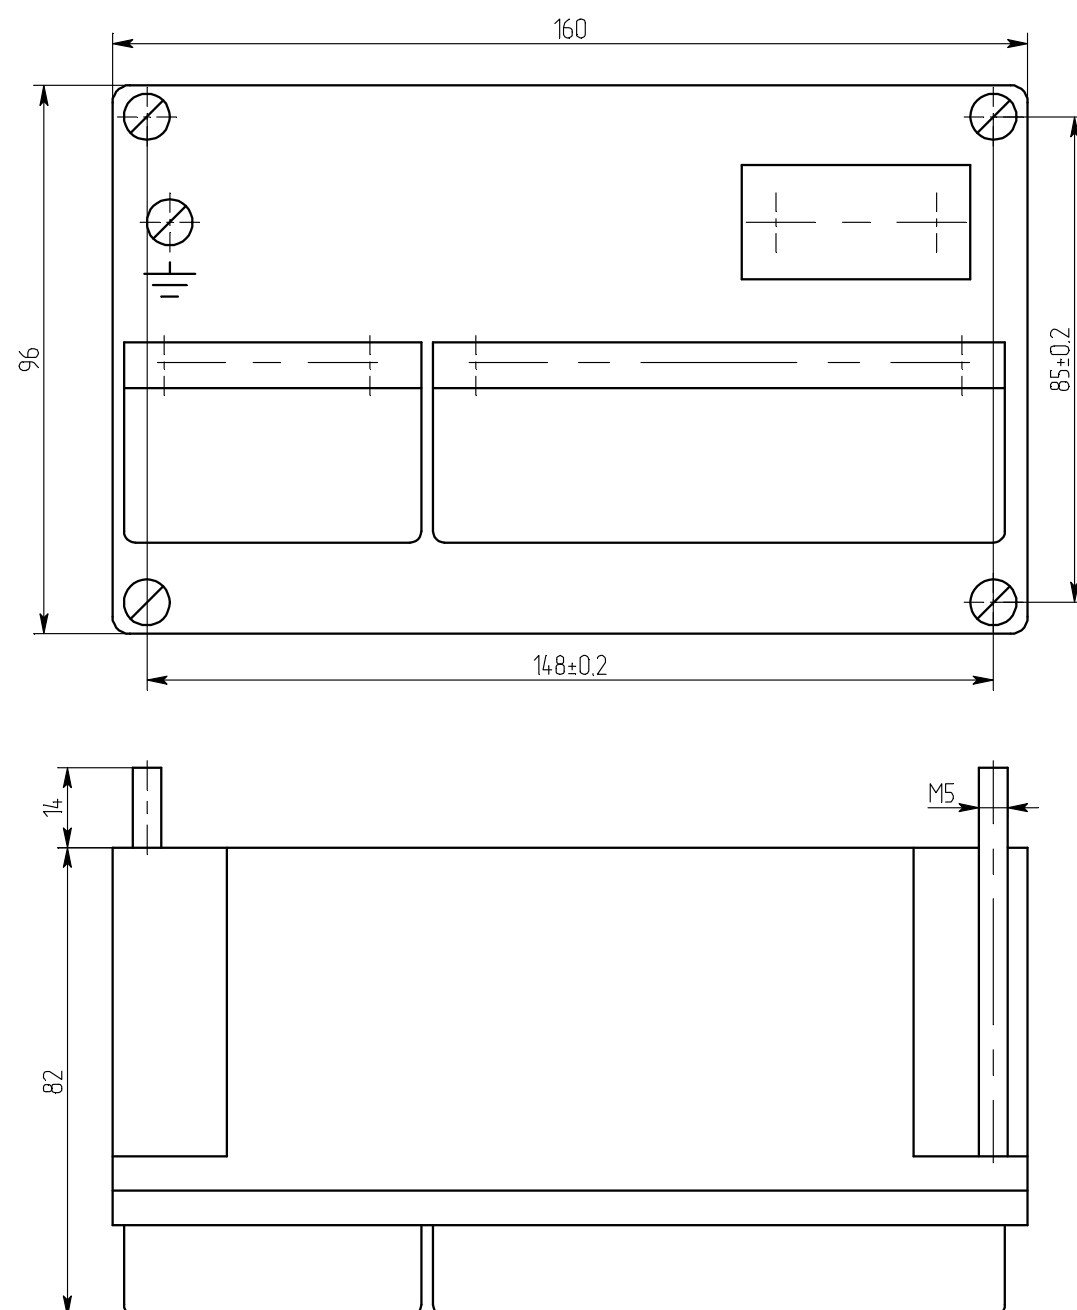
Габаритные и установочные размеры блока питания БП-20АМ1
